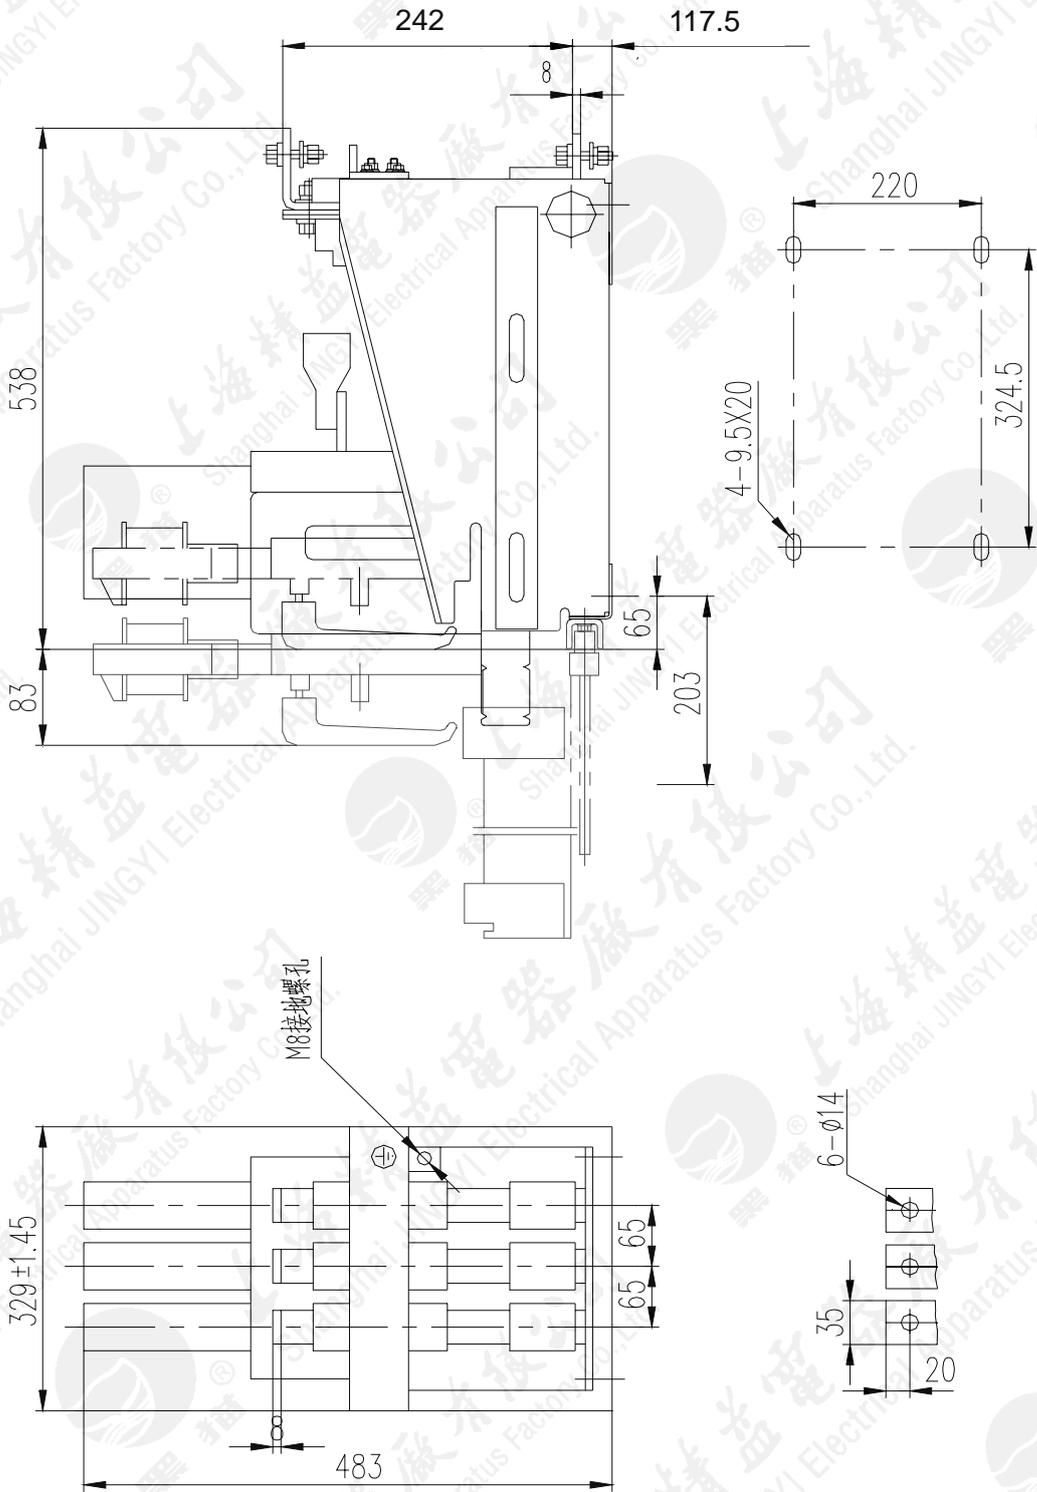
DW15C/DWX15C 抽屉式断路器安装尺寸及外形尺寸
